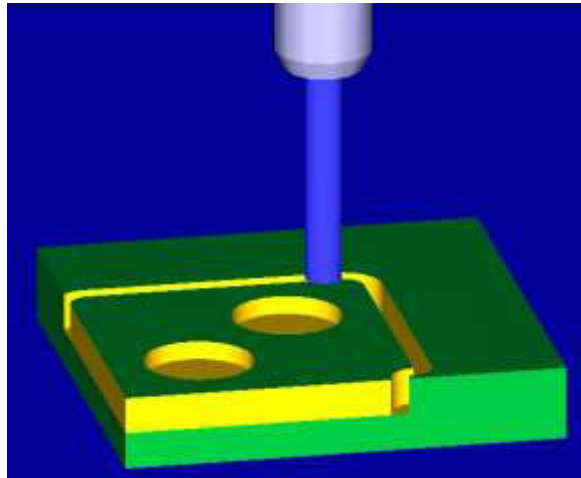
Ejemplo de maquinado en 2 dimensiones en fresadora CNC, maquinado de contornos y cavidades
